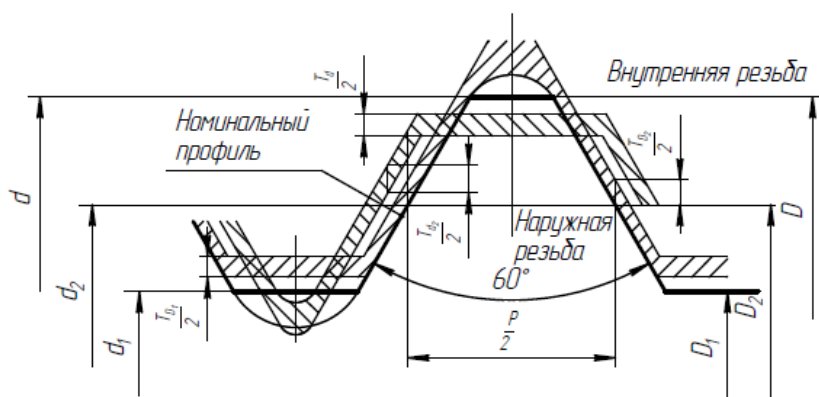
Расположение полей допусков метрической резьбы болта и гайки с натягом
